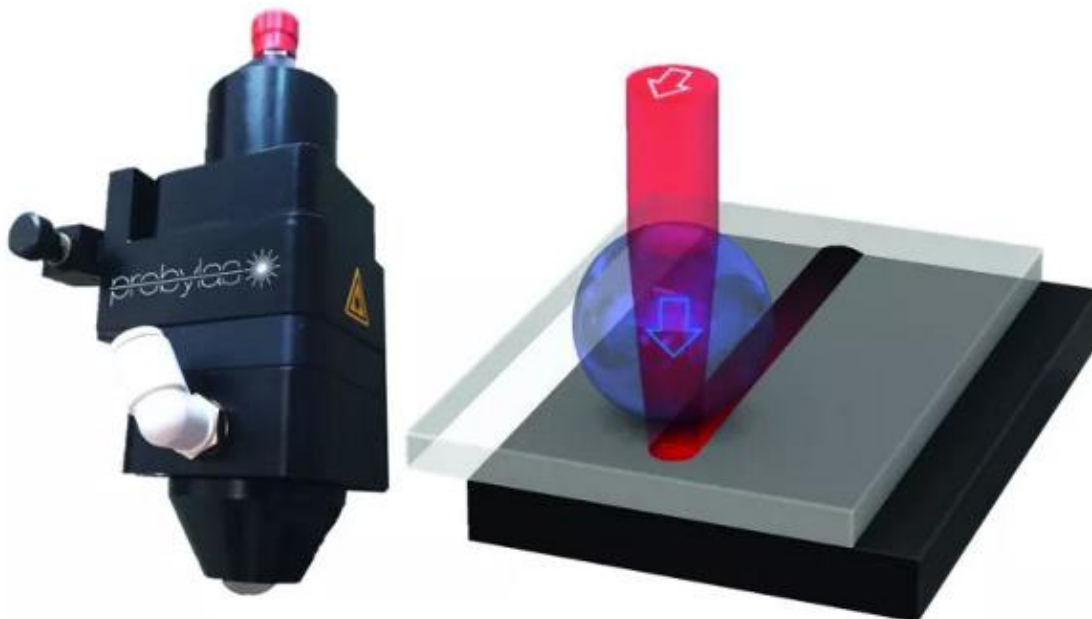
Prinzip LASER verschweißen mit Glaskugel
